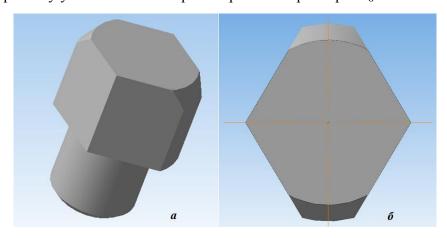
Срезанный палец: а – вид в 3-D; б – вид сверху
